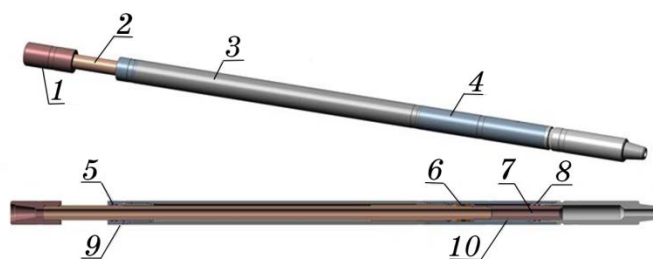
Інтенсифікатор яса: 1 – перевідник, 2 – шток, 3 – корпус верхній, 4 – корпус нижній, 5 і 8 – ущільнювач штока, 6 – ущільнювач циліндра, 7 і 9 – заглушка, 10 – хвостовик штока
